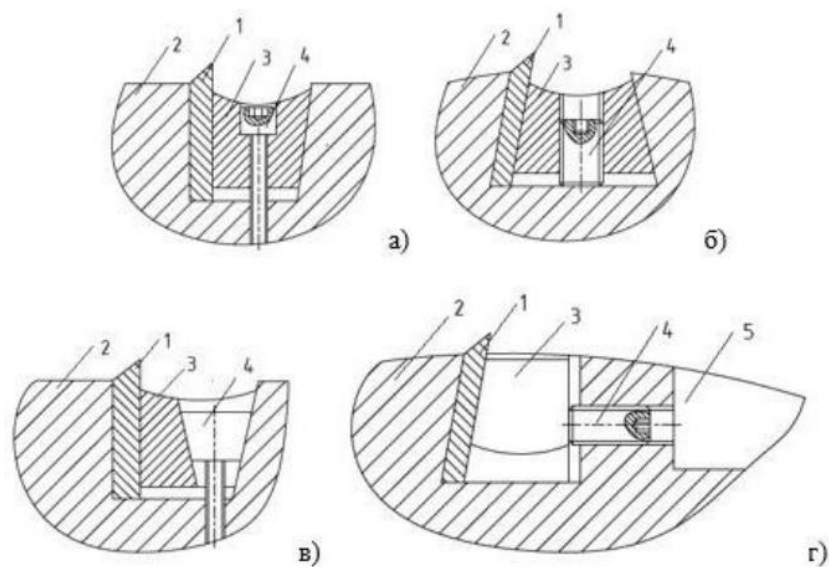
Види закріплення клином а)-диференціальний клин, б)-гвинт без шапки, в)-«половинчастий », г)-боковий, 1-пластина, 2-корпус фрези, 3- клин, 4- гвинт, 5 – канавка для гвинта [2].
